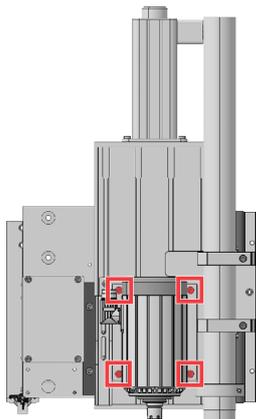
HERAUSSCHRAUBEN DER SCHRAUBEN
